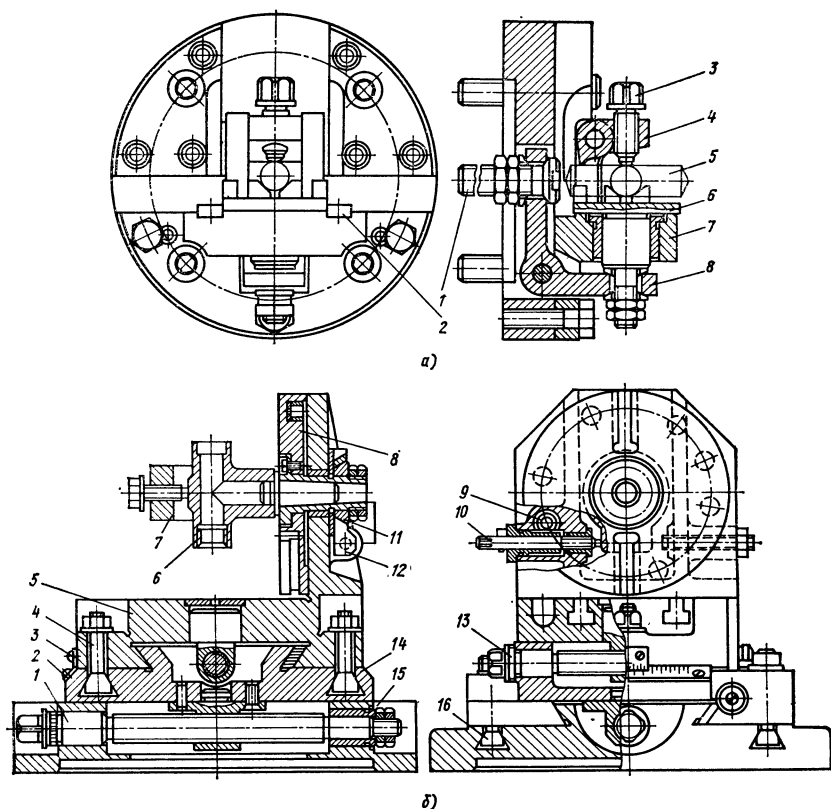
Специализированные наладочные приспособления для обработки тройников и крестовин:
